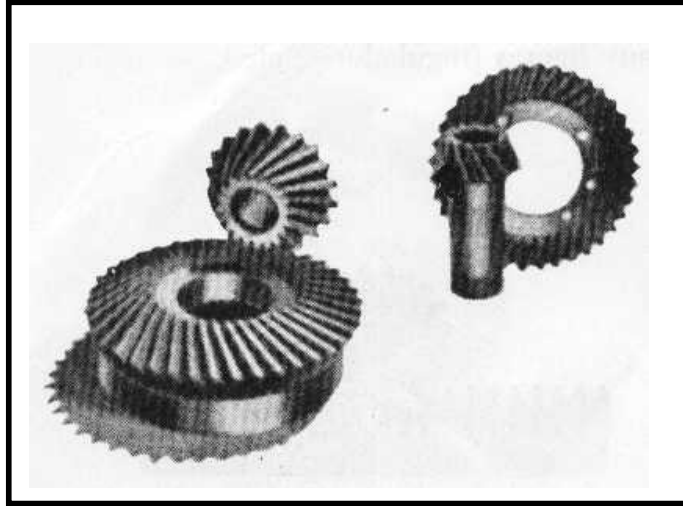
ENGRANAJES CÓNICO-HELICOIDALES
